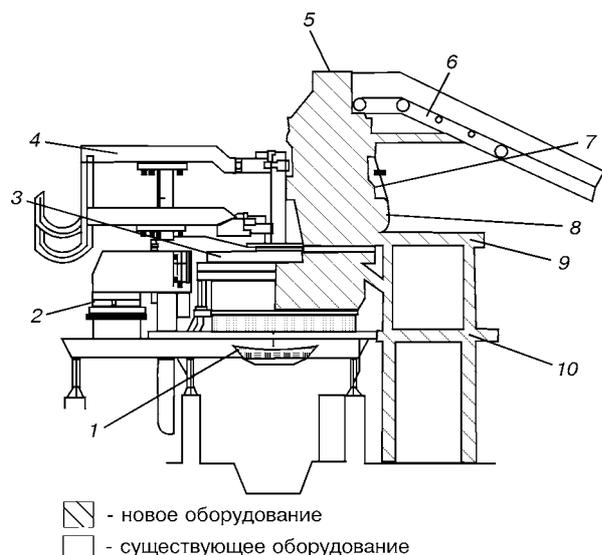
Схема шахтной дуговой печи с удерживающими пальцами: 1 — люлька; 2 — портал; 3 — свод; 4 — токопроводящие консоли; 5 — колпак отходящих газов; 6 — конвейер подачи скрапа; 7 — шахта/пальцы; 8 — механизм подъема/перемещения; 9 — стальная конструкция; 10 — площадка
